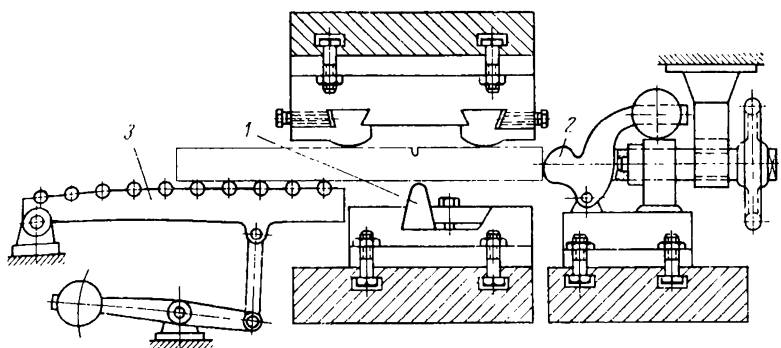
Приспособление для ломки с качающимся рольгангом и специальным упором: 1 — средний боек-опора; 2 — упор; 3 — качающийся рольганг
